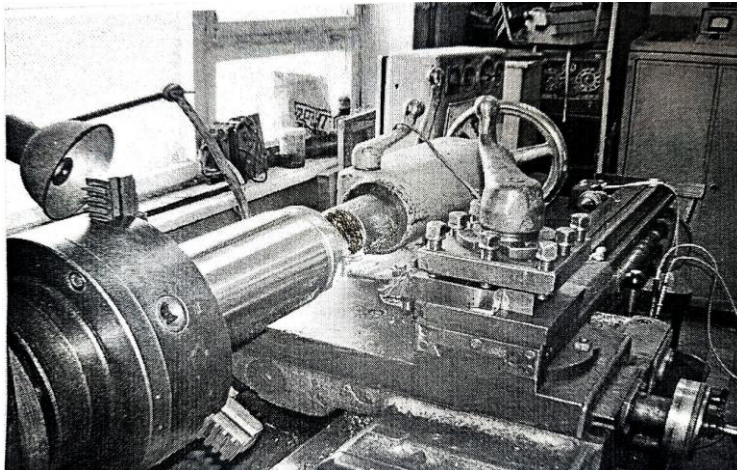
Общий вид станка с консольно закреплённой в патроне деталью
